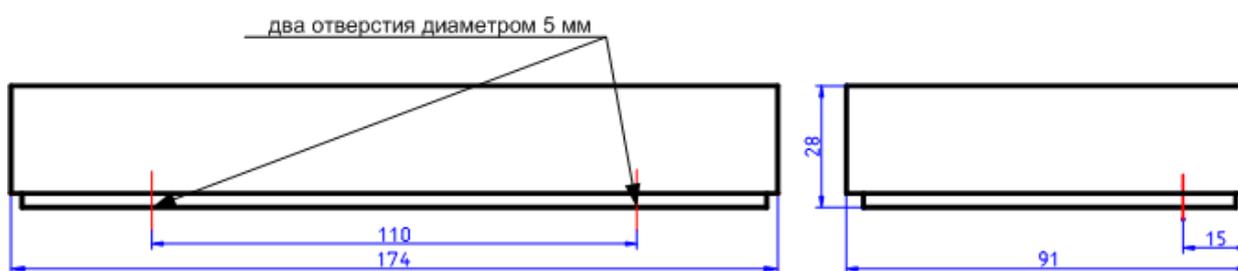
Корпус АБ4 без крышки и печатной платы
